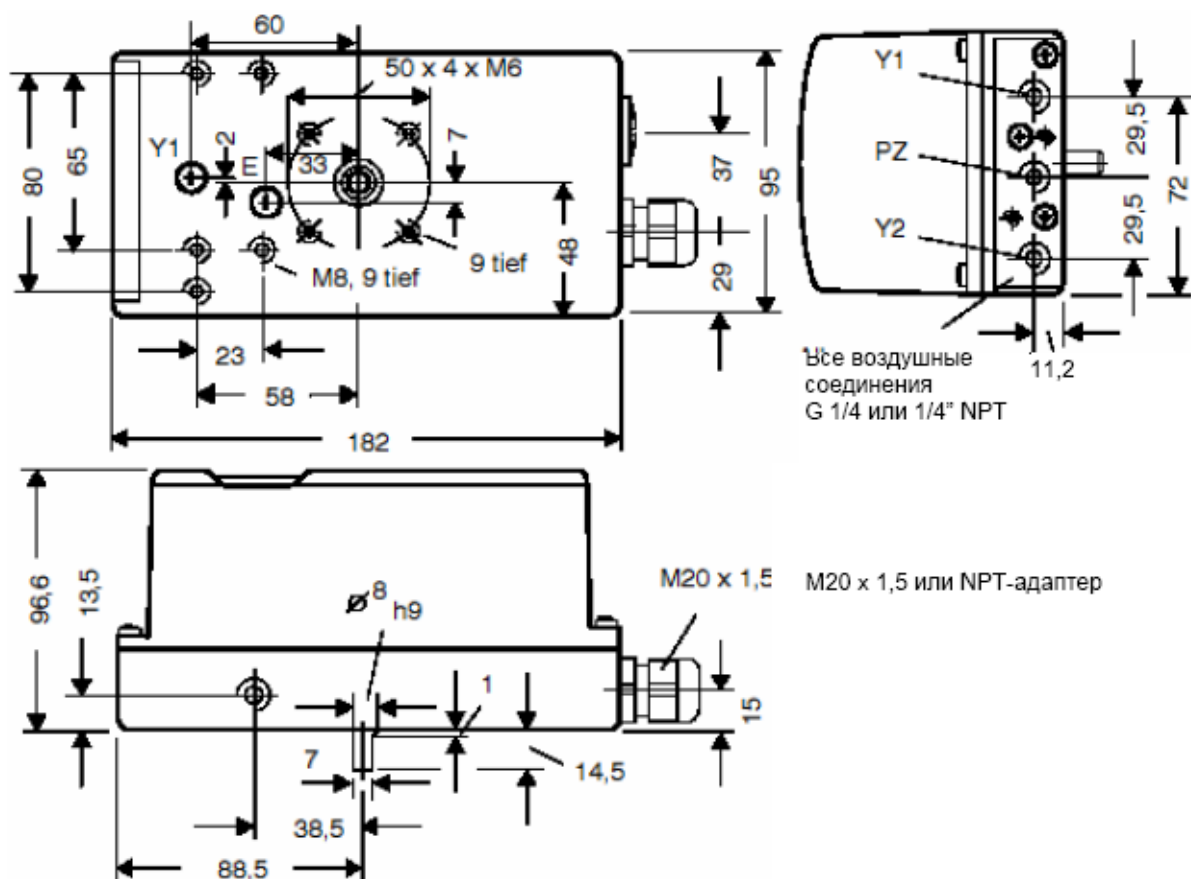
Габаритный чертеж конструкции в пластиковом корпусе 6DR5xx0
